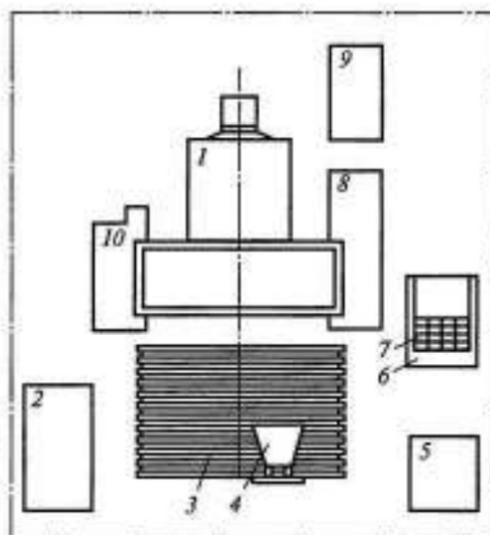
Схема организации рабочего места шлифовщика, обслуживающего плоскошлифовальный станок:
